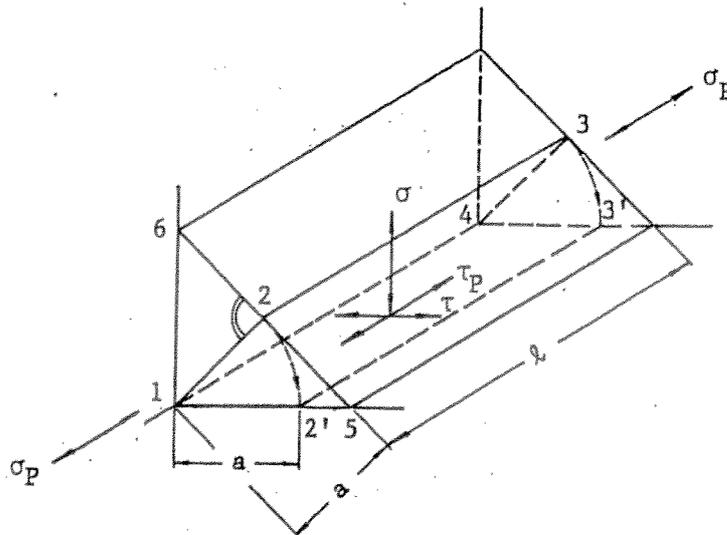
Soldadura de filete idealizada, posibles direcciones de tensiones en el corte longitudinal 1, 2', 3', 4 y en la sección de corte 1-5-6 perpendicular.
